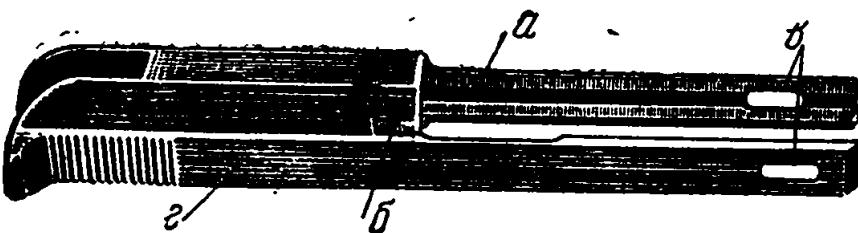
Затвор: *а* — направляющие выступы и пазы; *б* — выбрасыватель; *в* — прорези для замыкателя; *г* — полукруглый вырез для разобщителя
